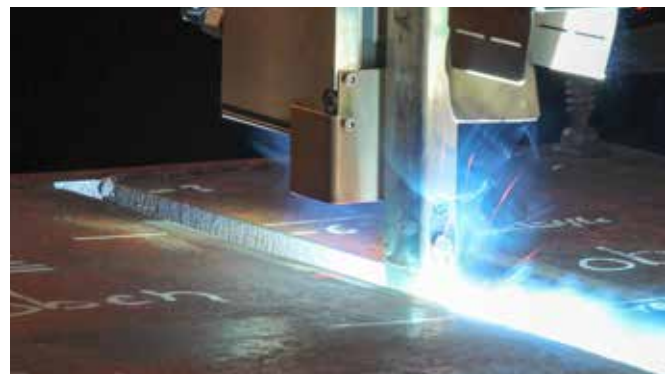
MSG-Engspaltschweißen am Demonstrator mit 50 mm Blechdicke
